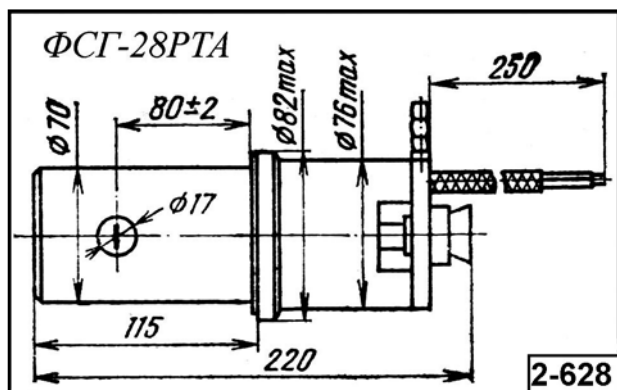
Внешний вид и габаритные размеры охлаждаемого фоторезистора ФСГ-28РТА
